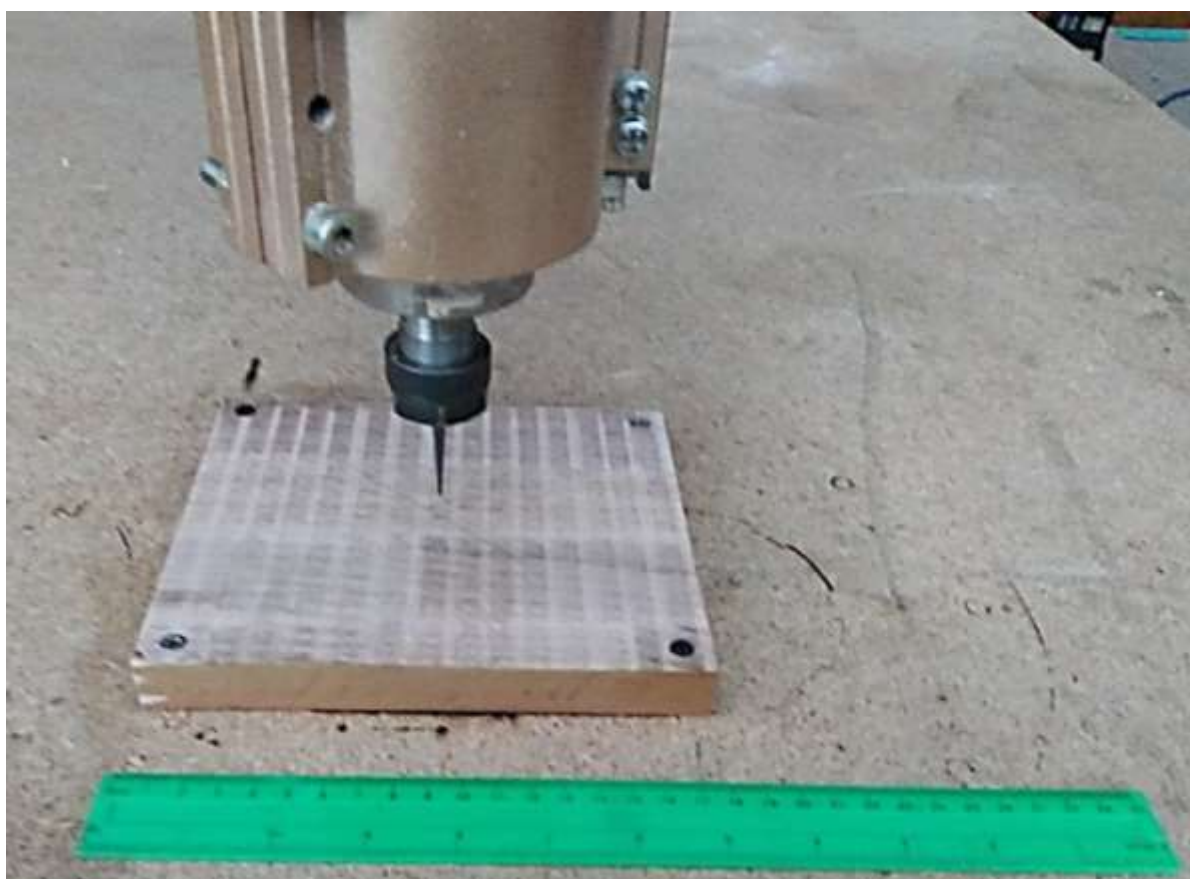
Кріплення заготовки на столі фрезерного верстата з ЧПК
